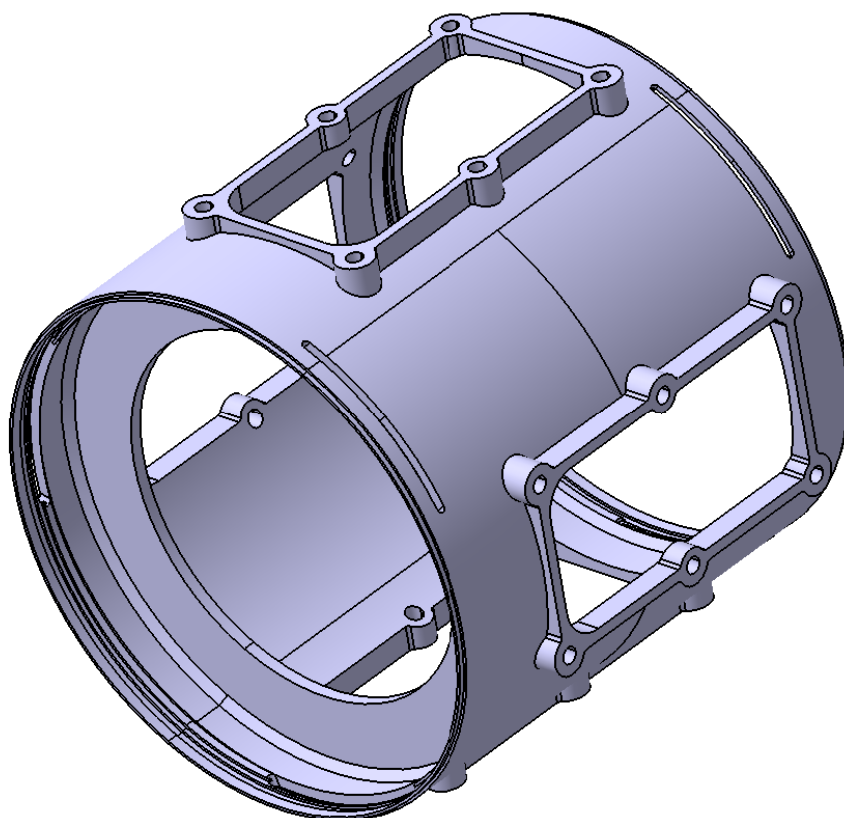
Трехмерная модель детали «Корпус центральный»
